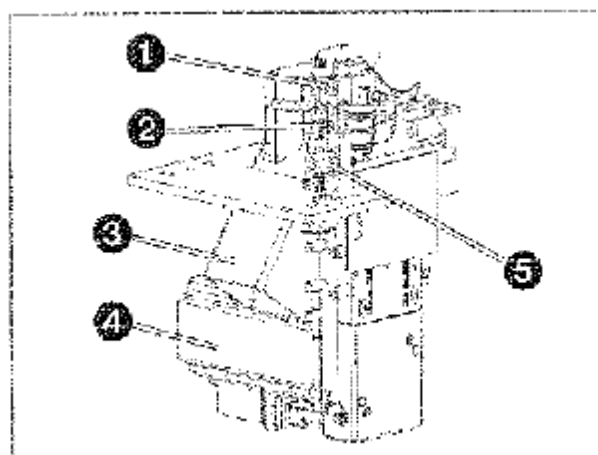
Ріжуча головка: 1 - верхній блок лез; 2 - нижній блок лез; 3 - канал для залишків зачистки; 4 - привідний двигун; 5 - заправляючий пристрій
